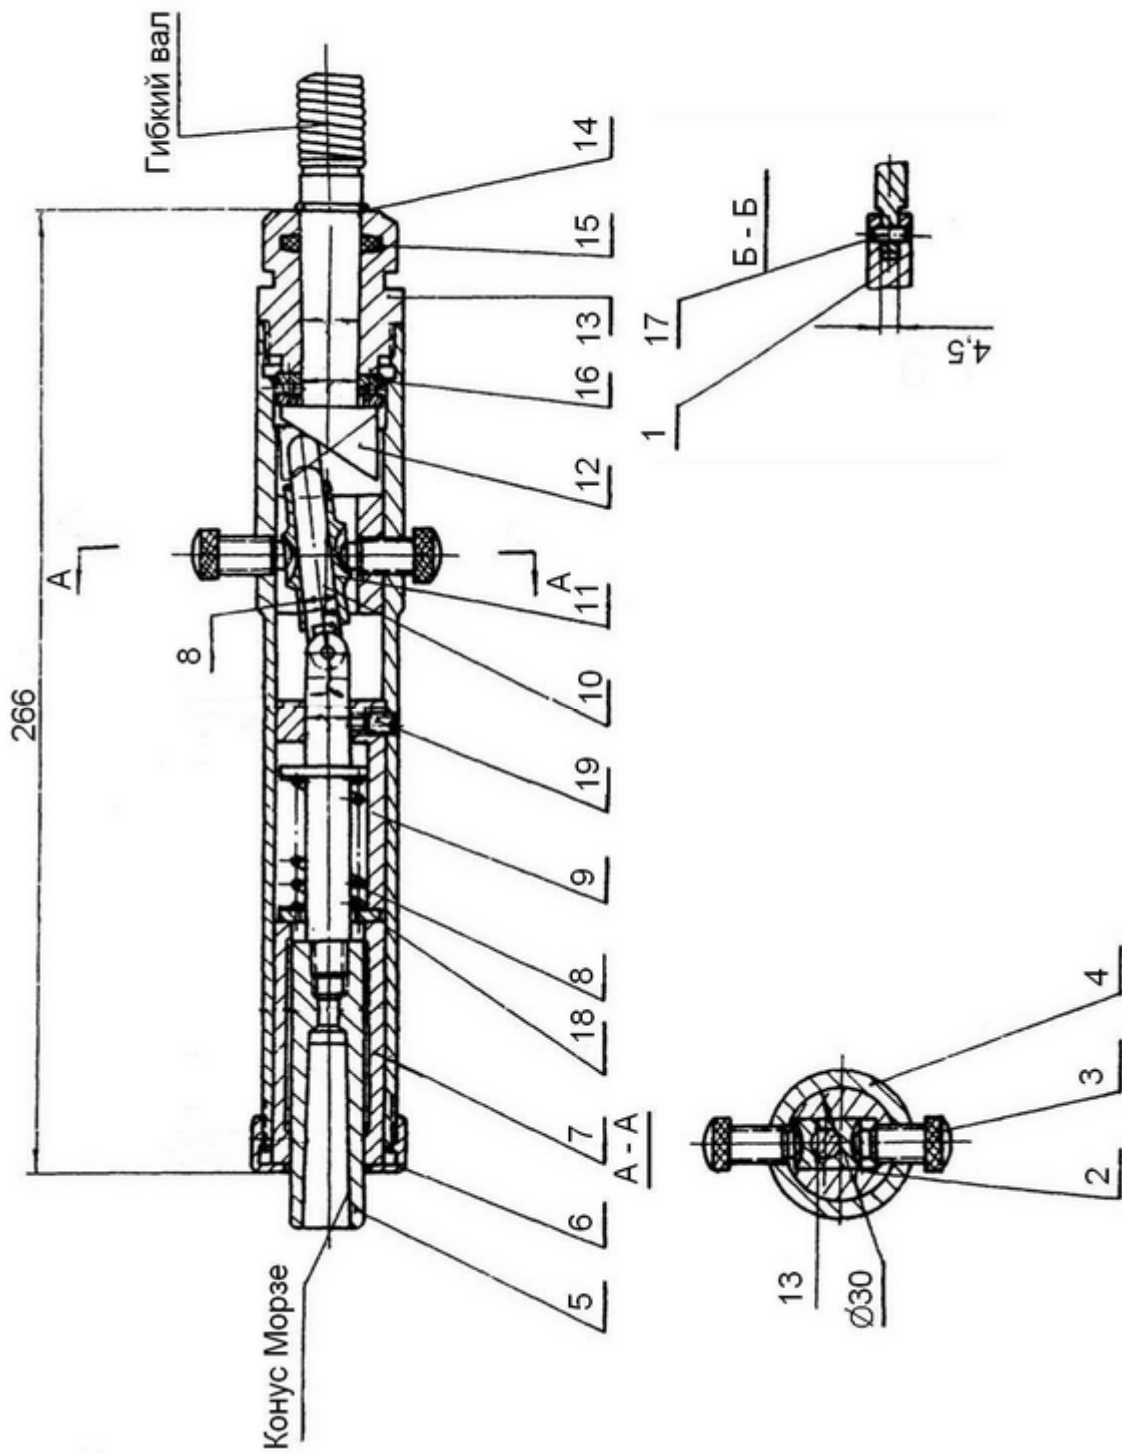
Приспособление для механического шабрения СД 7802 – 4001
